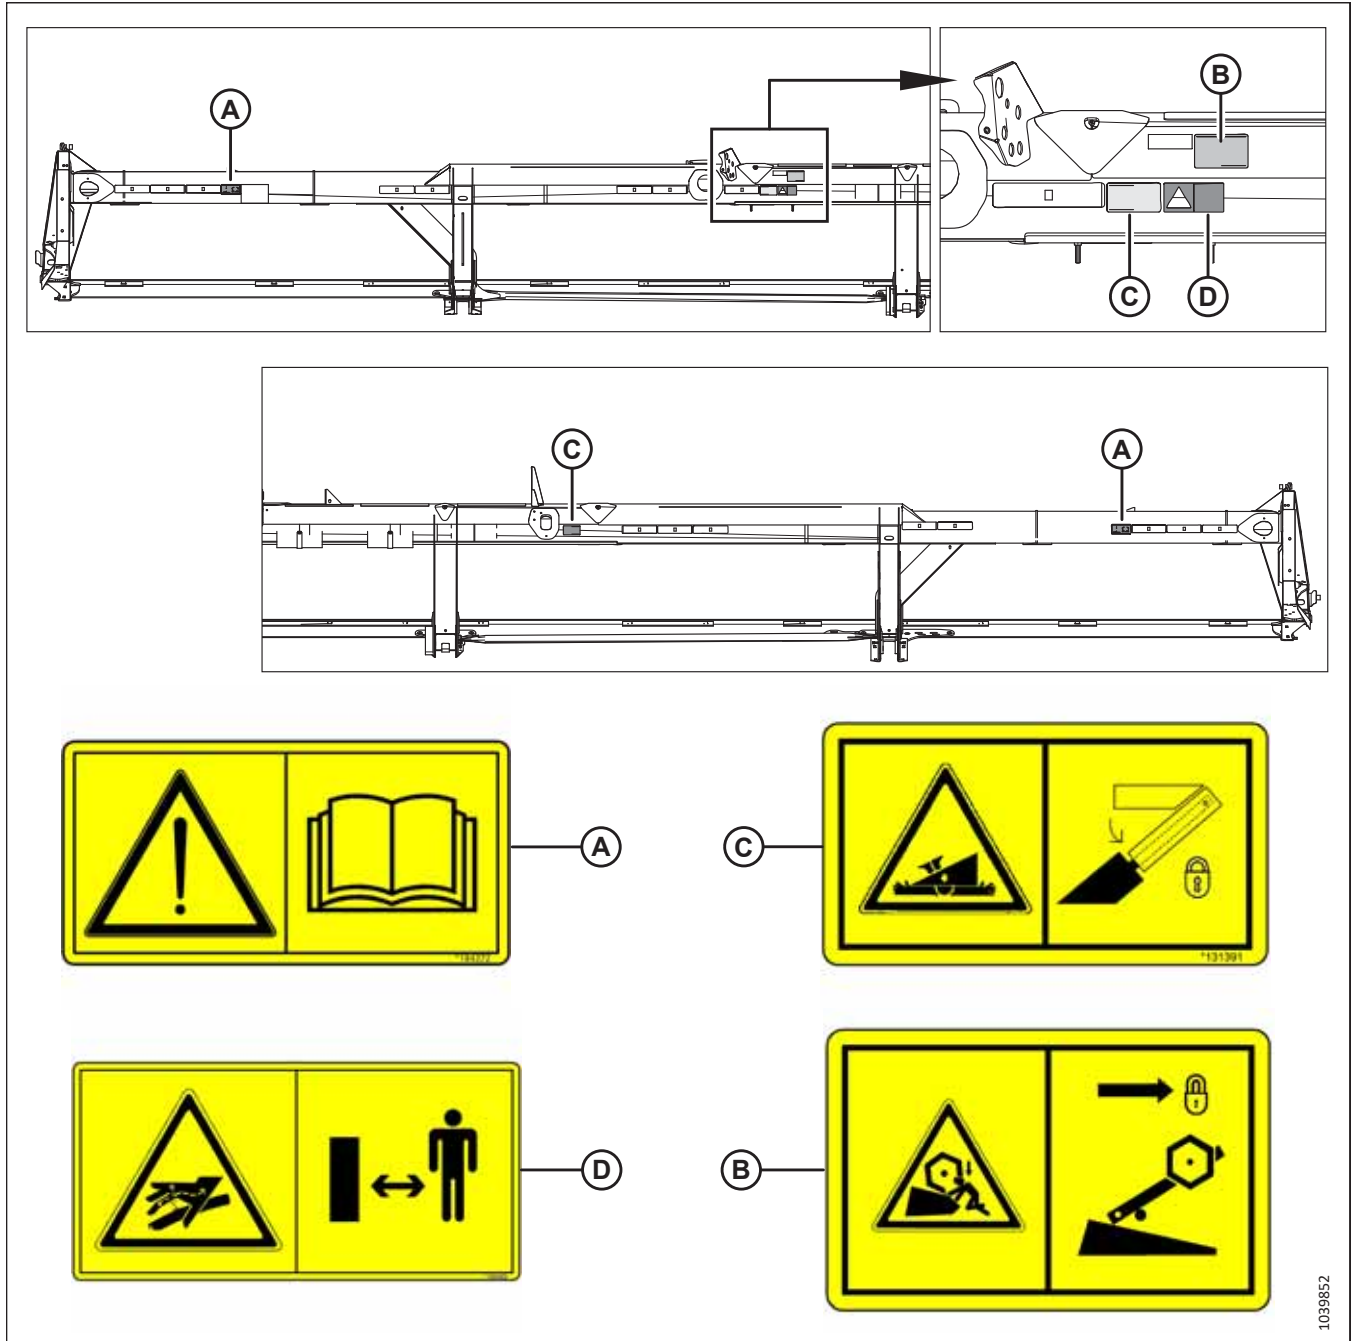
Tube arrière – Plateforme rigide de 12,1 m (45 pi)
